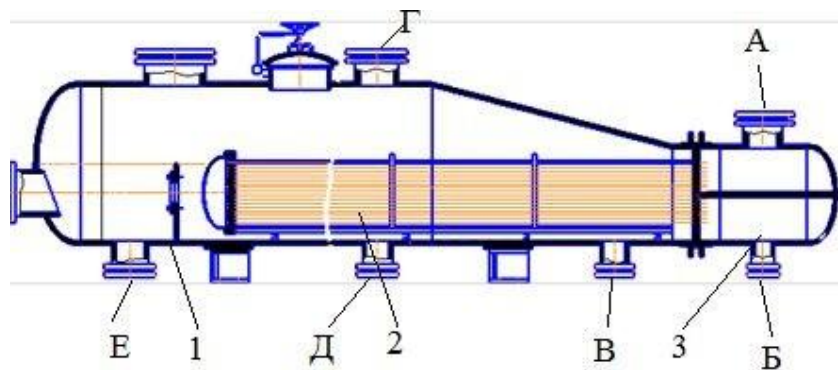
Конструкція випарника з паровим простором 1 – корпус; 2 - трубний пучок; 3 – розподільна камера
